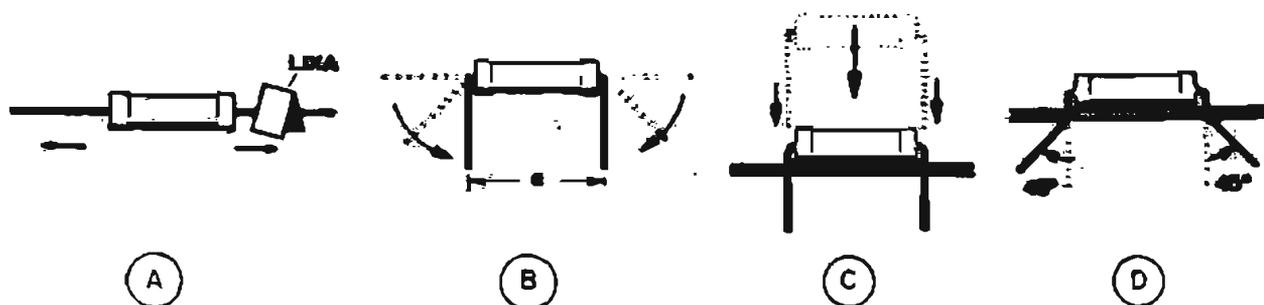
Preparação, montagem e fixação mecânica de componentes numa placa de fiação impressa
